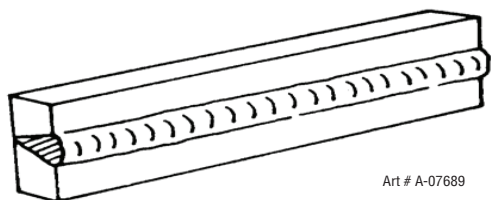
Position horizontale, soudure bout à bout
